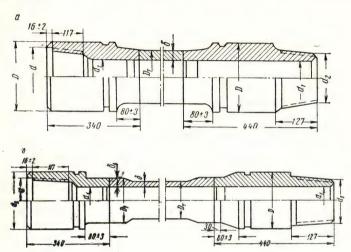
Бурильные трубы с приваренными соединительными концами: a — типа ТБП; b — типа ТБПВ; b — раструб; b — турба; b — ниппель
